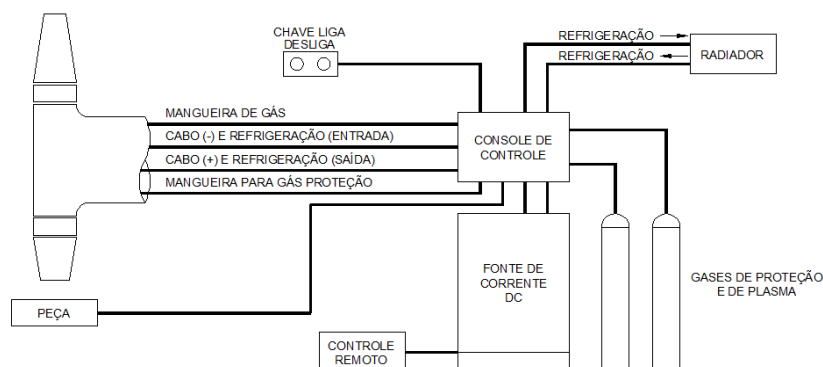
Diagrama esquemático da soldagem a plasma. Baseado em [2].
